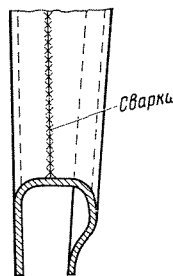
Соединение листов топки вокруг шуровочного отверстия сварным швом
